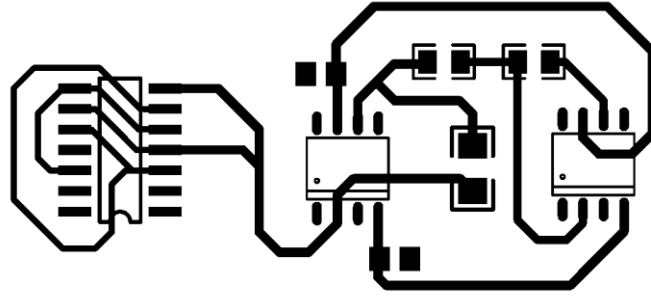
利用 EasyEDA 軟體轉換出之 PCB layout 圖。首先在設計圖中定義好所有元件連接、封裝型號與數值，再轉換至 PCB Layout 模式進行元件排列與走線，此電路為本研究設計之 pH 值感測電路 layout 圖。
